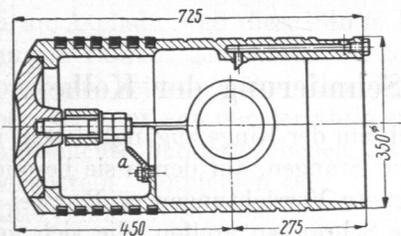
Gasmaschinenkolben mit besonders eingesetztem Boden.
